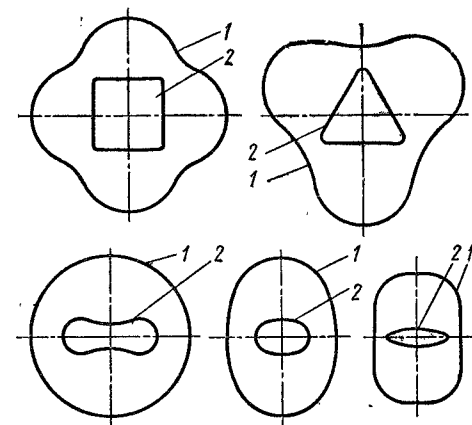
Формы заготовок при вытяжке глубоких коробчатых деталей различного сечения: 1 — заготовки; 2 — сечение деталей
